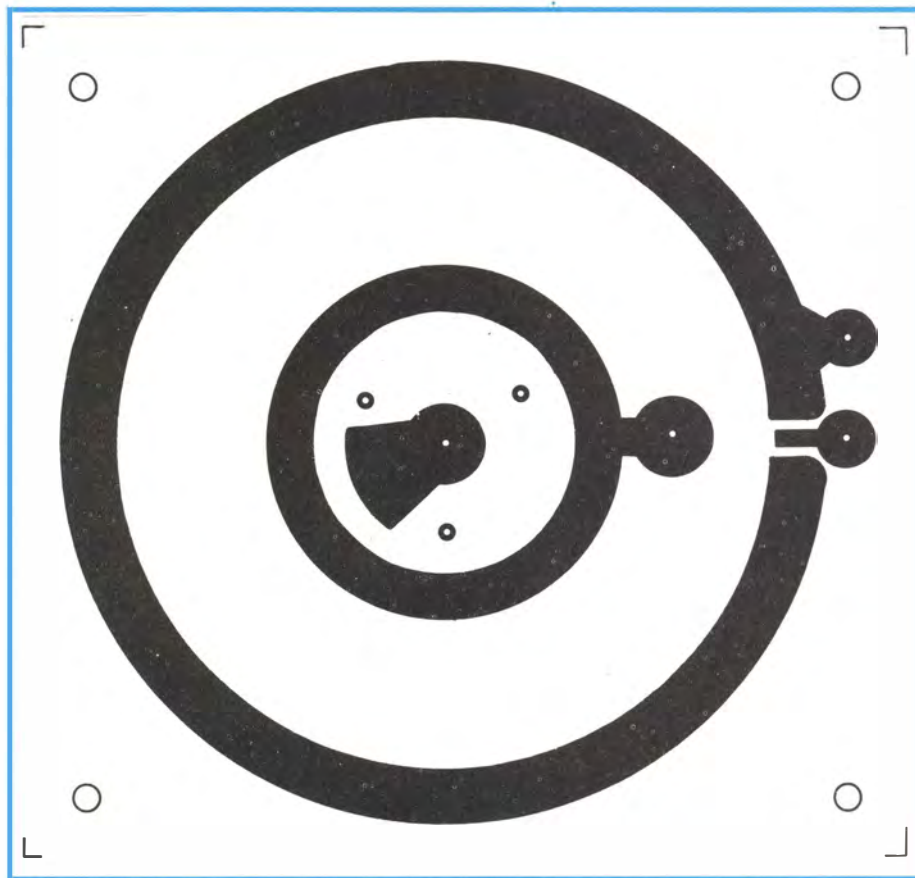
Basetta a circuito stampato del supporto motore in scala 1:1
